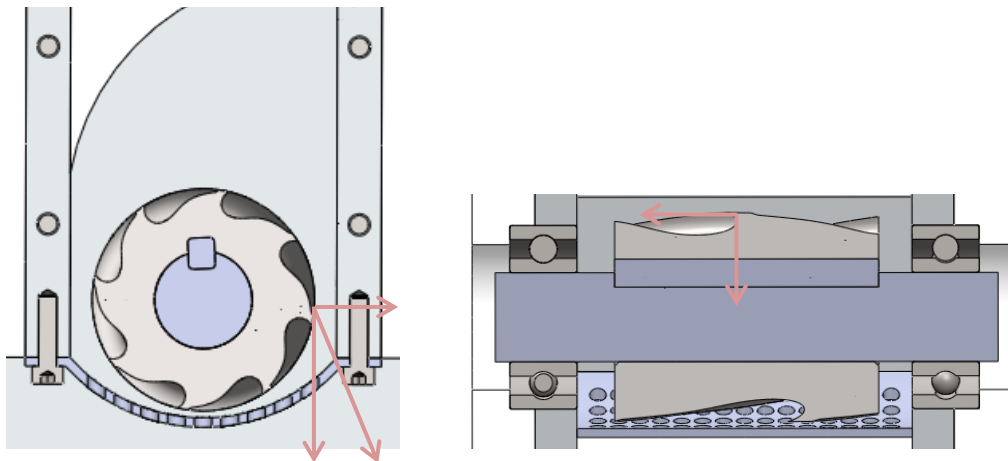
Cargas aplicadas sobre la estructuras de aluminio [Fuente propia]
